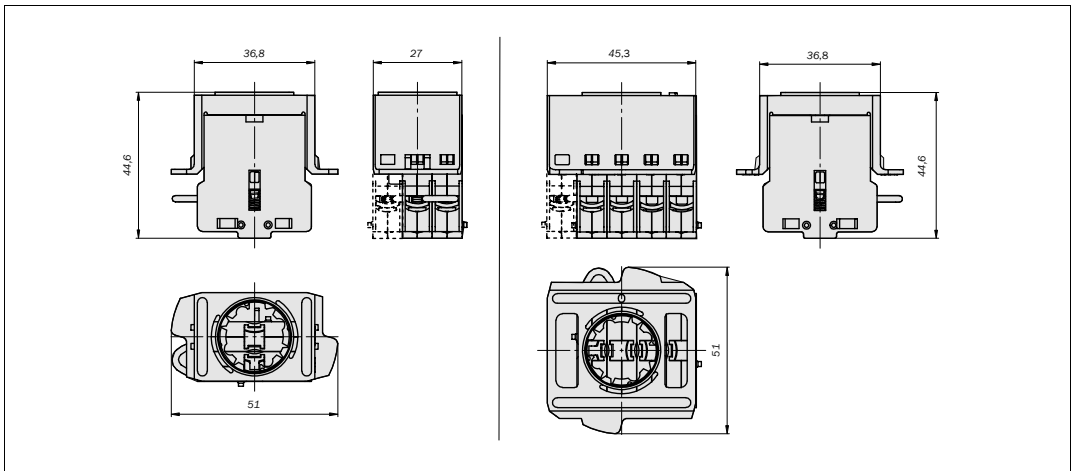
Croquis de dimensiones de los bloques de contacto (mm)
